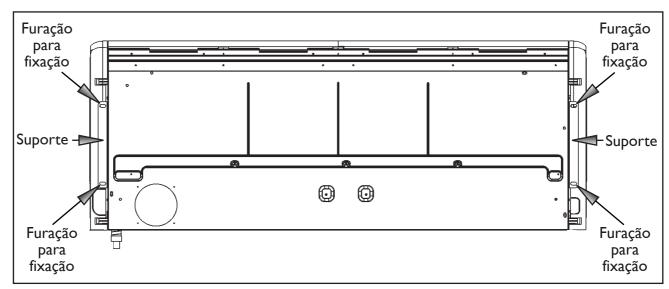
SUPORTES E FURAÇÃO PARA FIXAÇÃO
